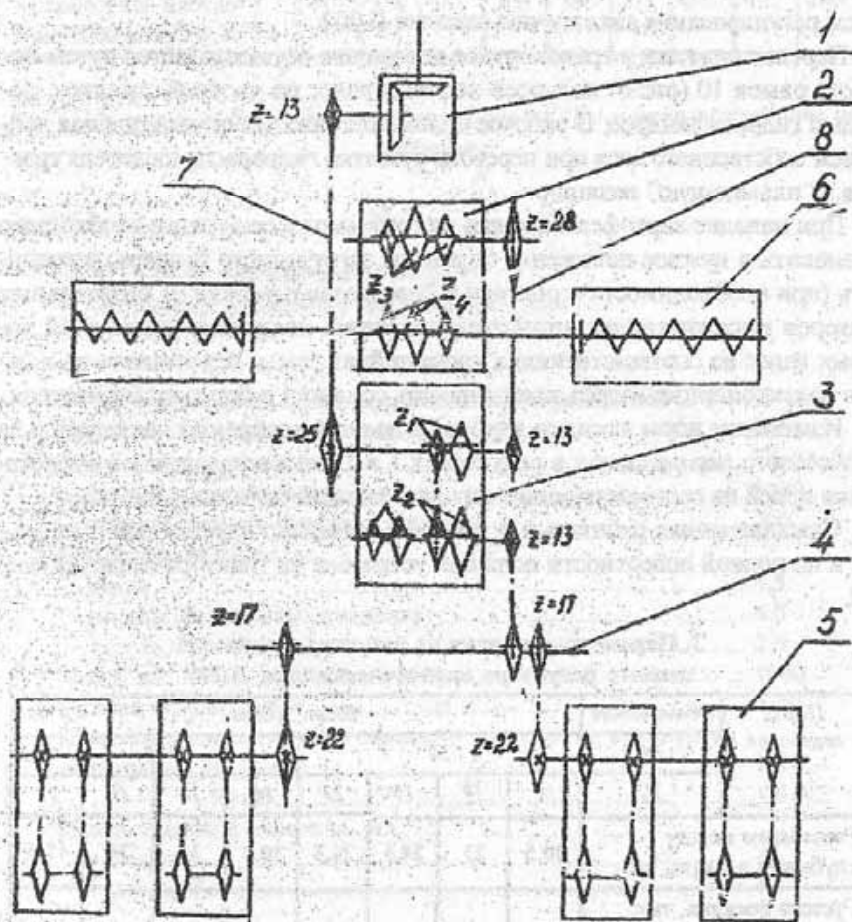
Кинематическая схема картофлесажалки Л-207: 1 — конический редуктор; 2 — цепной редуктор привода туковысевающего оборудования; 3 — цепной редуктор привода высаживающих аппаратов; 4 — контрпривод; 5 — высаживающие аппараты; 6 — туковысевающее оборудование; 7,8 — цепи.
